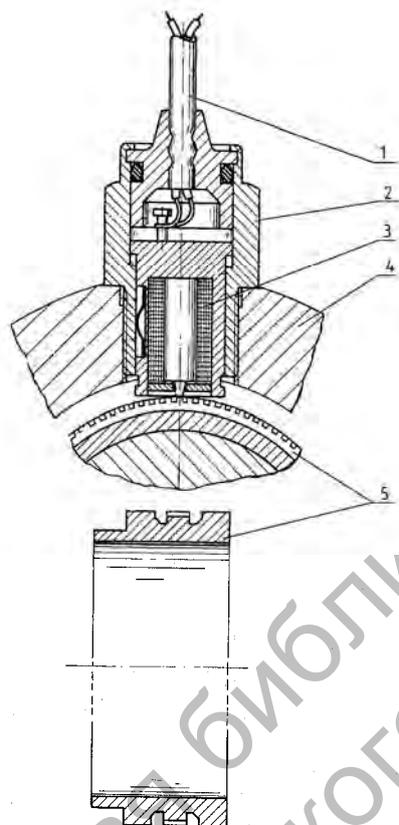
Датчик угловой скорости колеса в разрезе [13]: 1 – электрический кабель; 2 – корпус датчика; 3 – катушка; 4 – неподвижный корпус; 5 – ротор зубчатый
